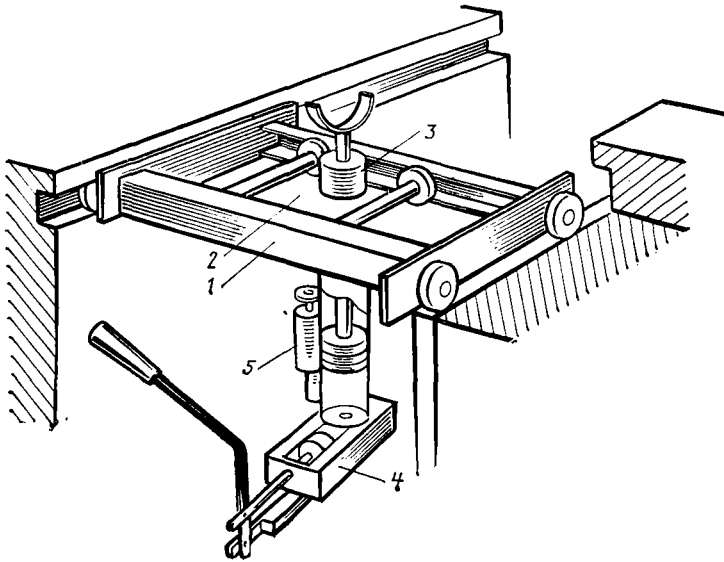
Канавный одноплунжерный гидравлический подъемник:
